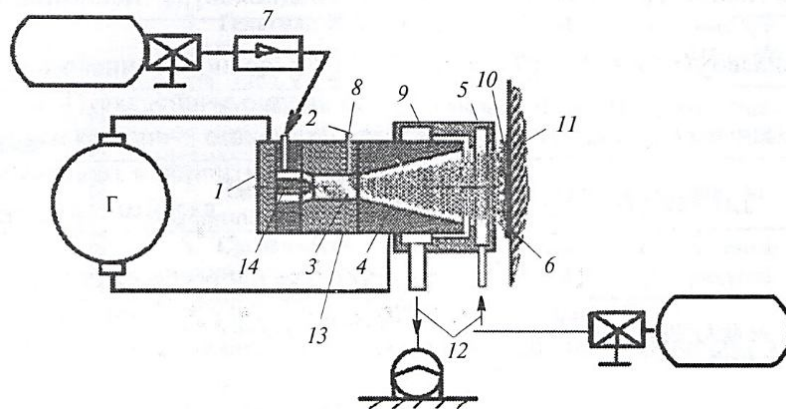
Схема газоплазменого покриття робочої поверхні інструменту преса:
